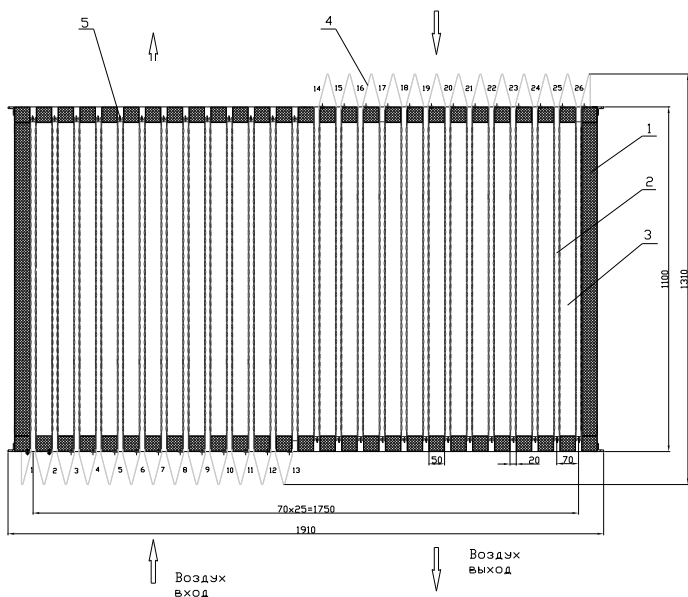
Масообмінний модуль: 1 – корпус; 2 – канали; 3 – зневоднюваний матеріал; 4 – напрямні входу сушильного агента; 5 – керовані стулки
